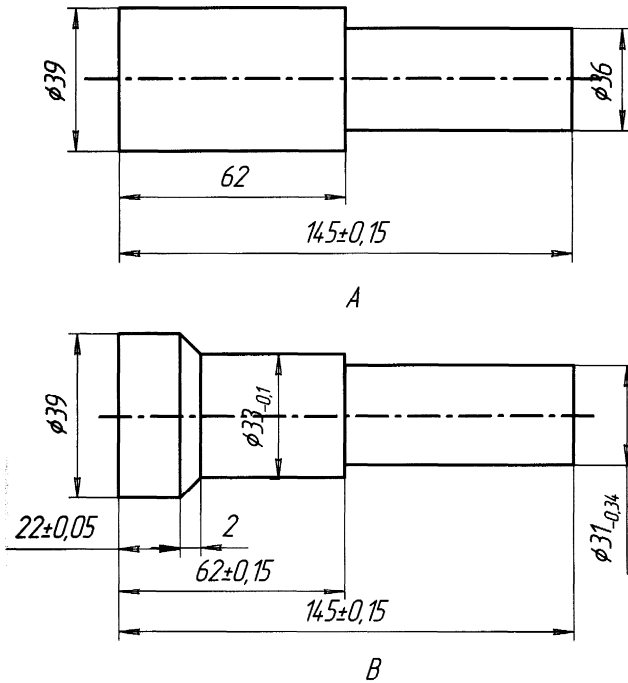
Эскизы заготовки (А) и детали (В) [15]
